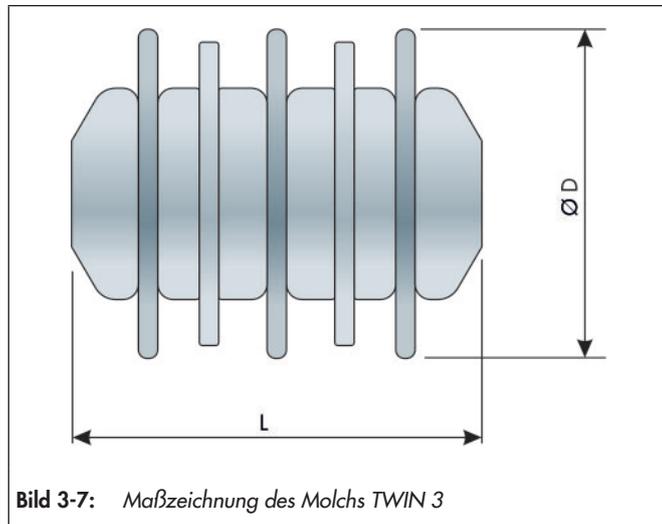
Maßzeichnung des Molchs TWIN 3
